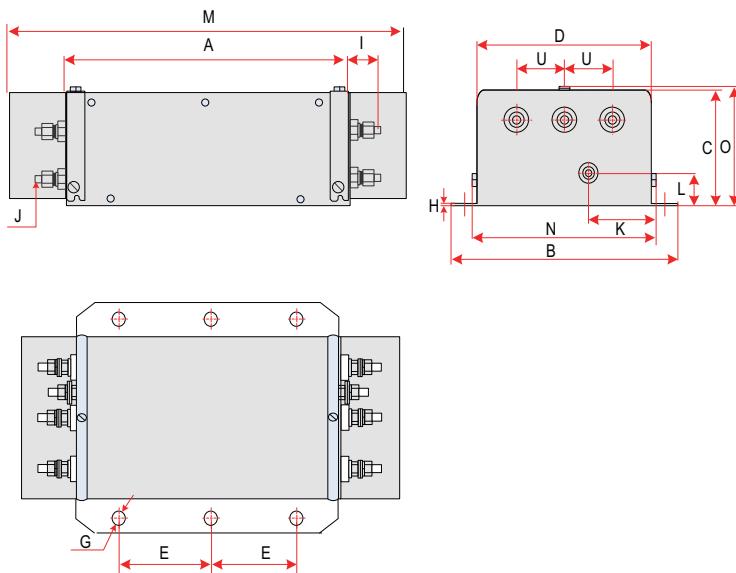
FN3258系列50-180A滤波器尺寸图(单位: mm)
